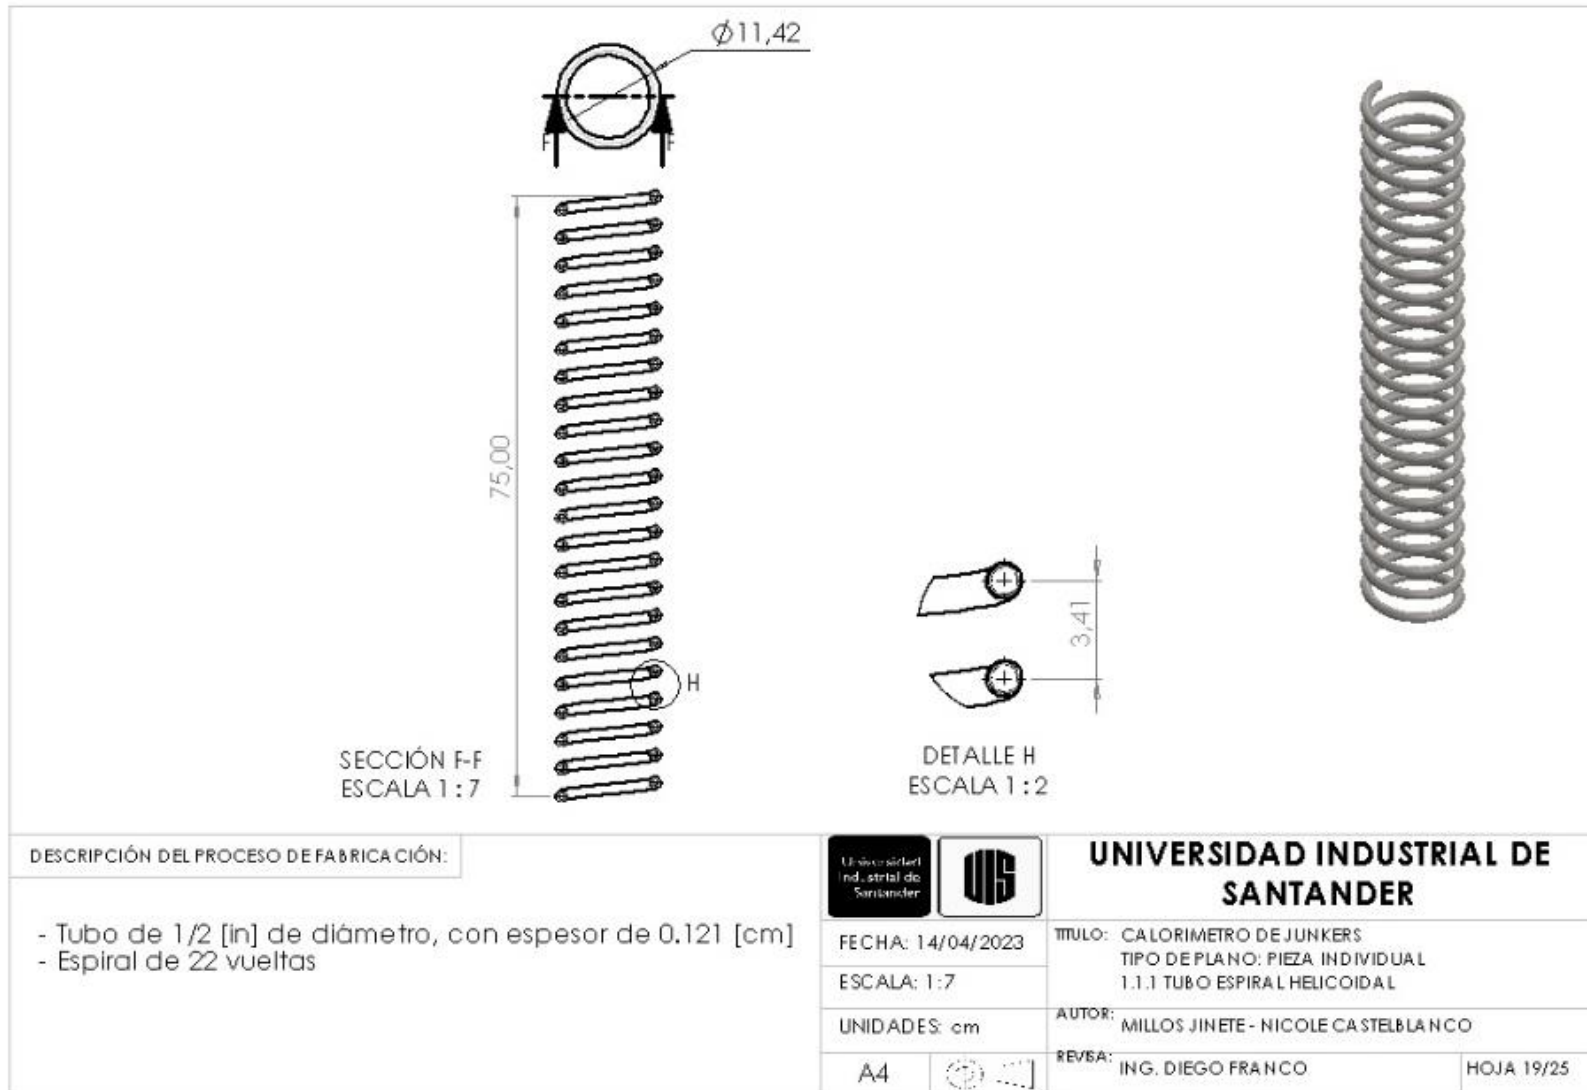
Plano vista isométrica conjunto accesorio espiral.
